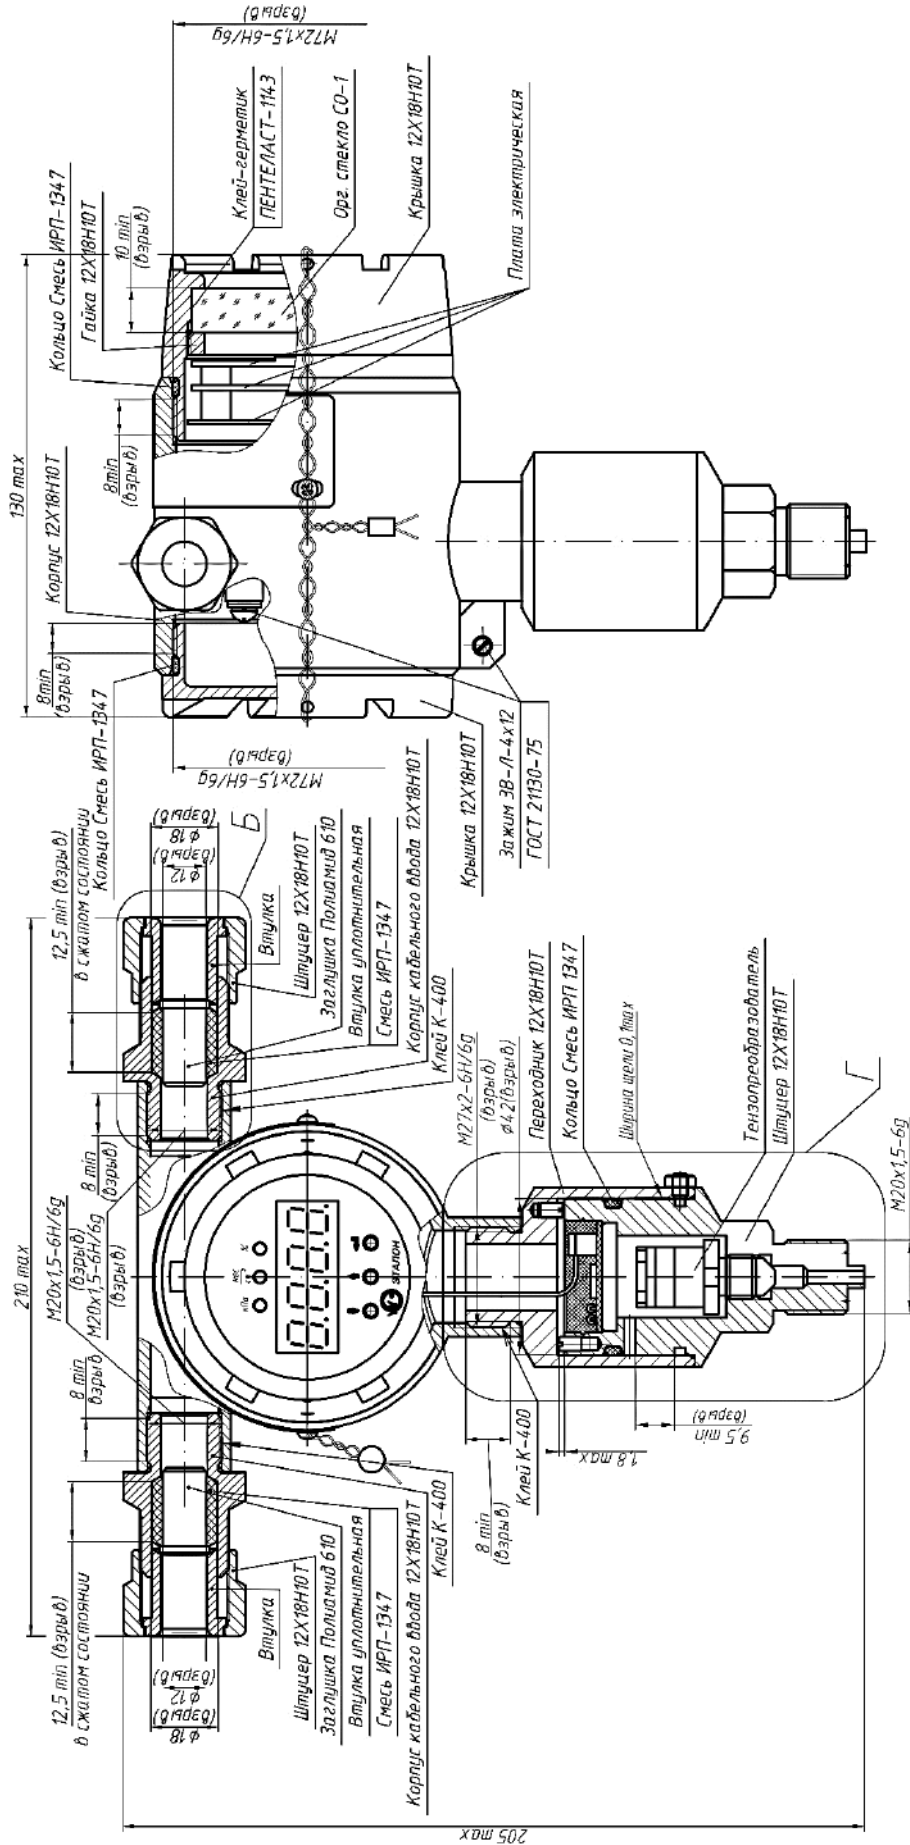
Чертеж взрывозащиты датчиков в корпусе из нержавеющей стали
